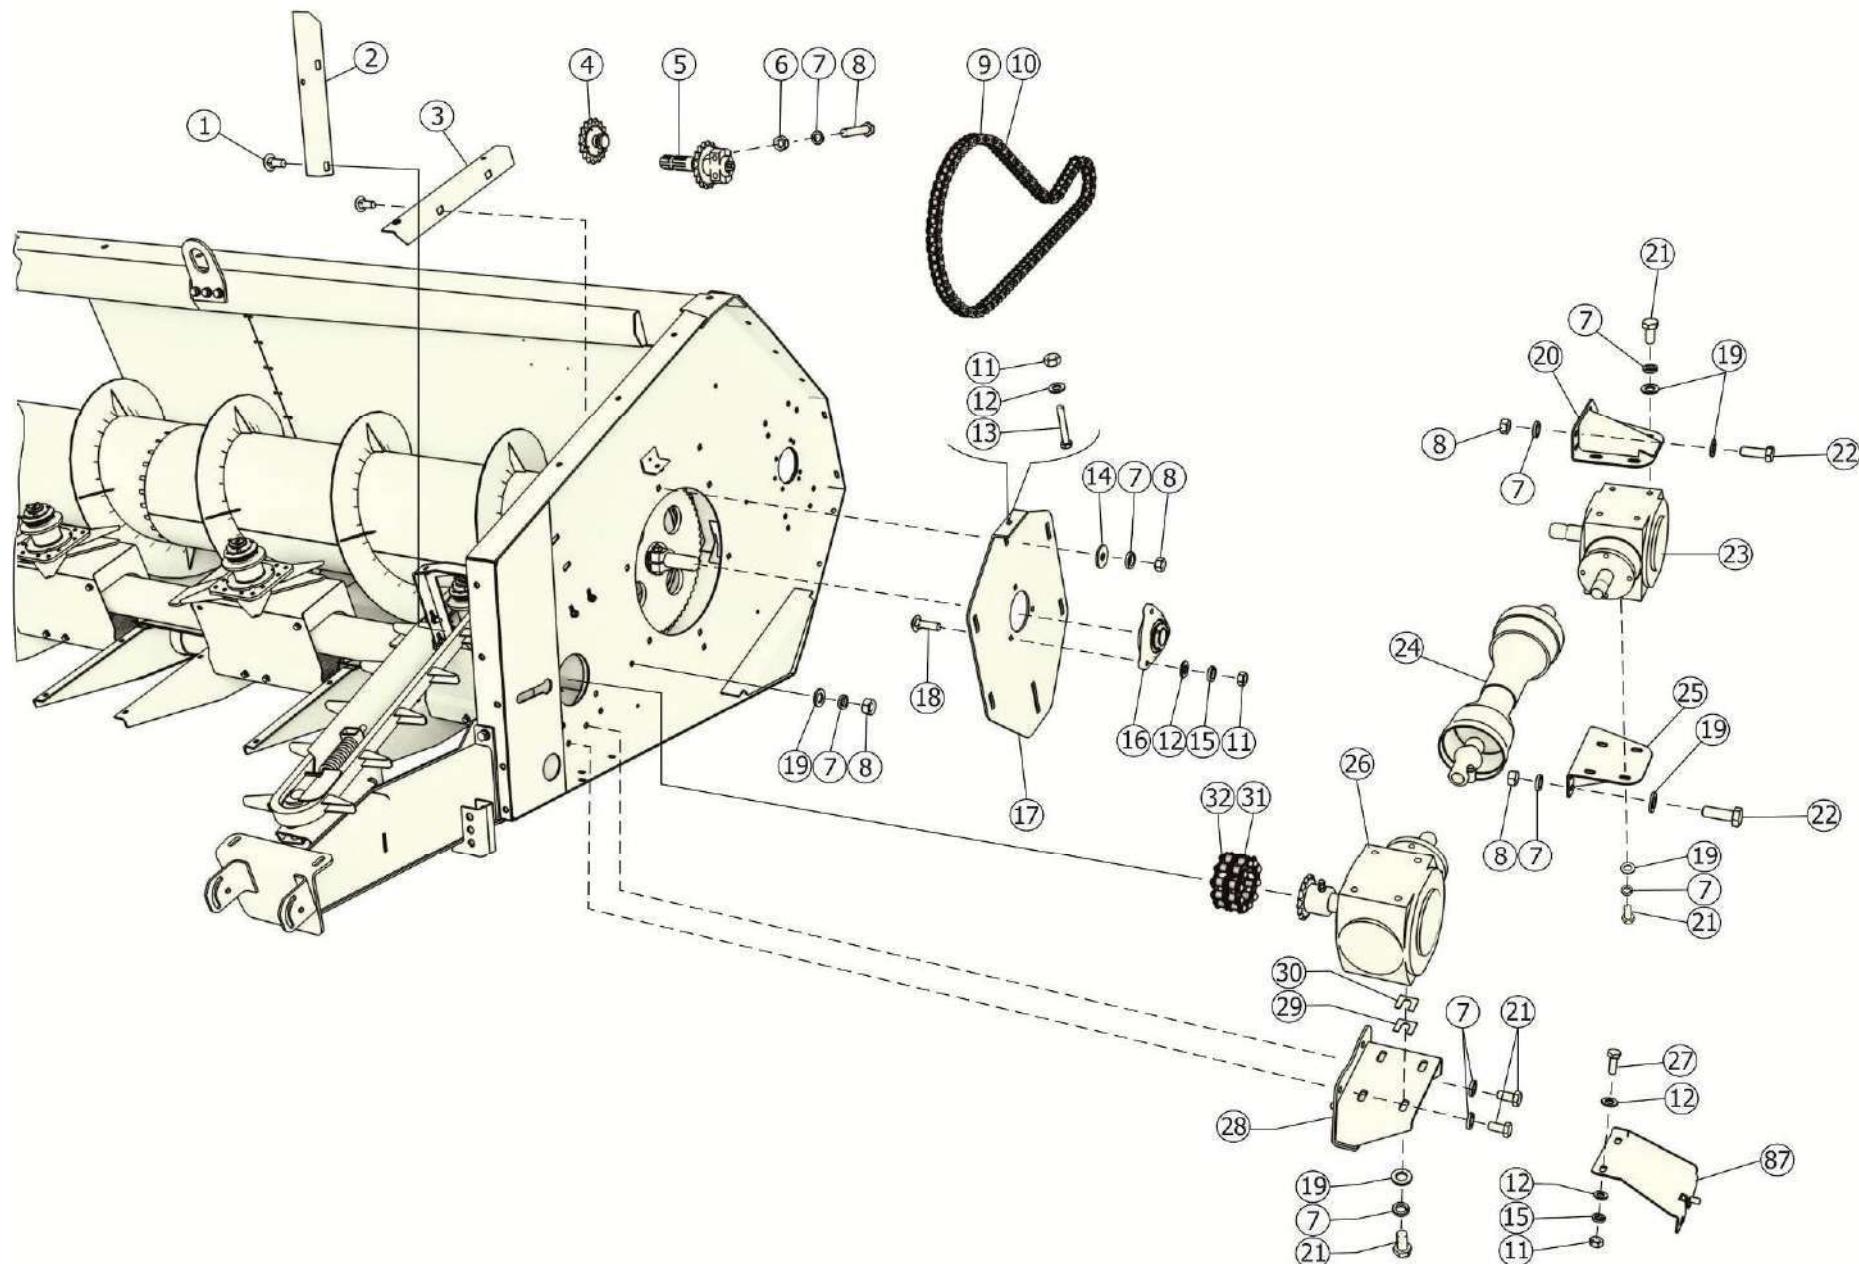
Корпус ПСП-810.01.01.000А. Вид слева
